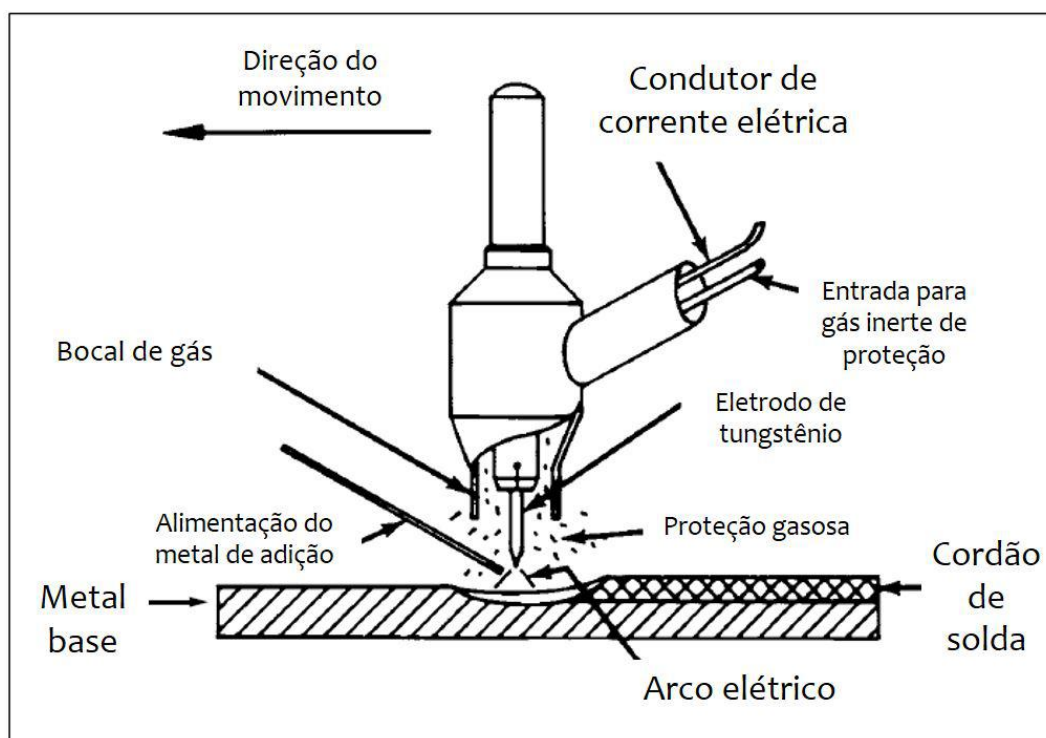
Desenho esquemático de uma operação manual de uma soldagem com GTAW (Adaptado de [28]).
